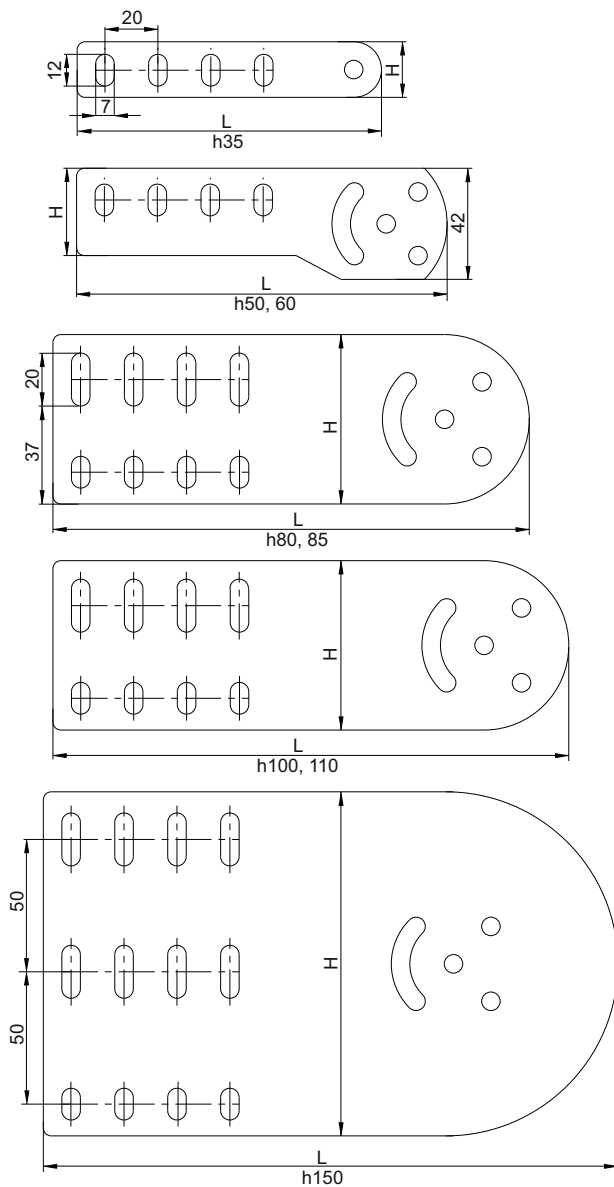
Пластина шарнирного соединения / Figure 3 – Hinge-jointed plate
